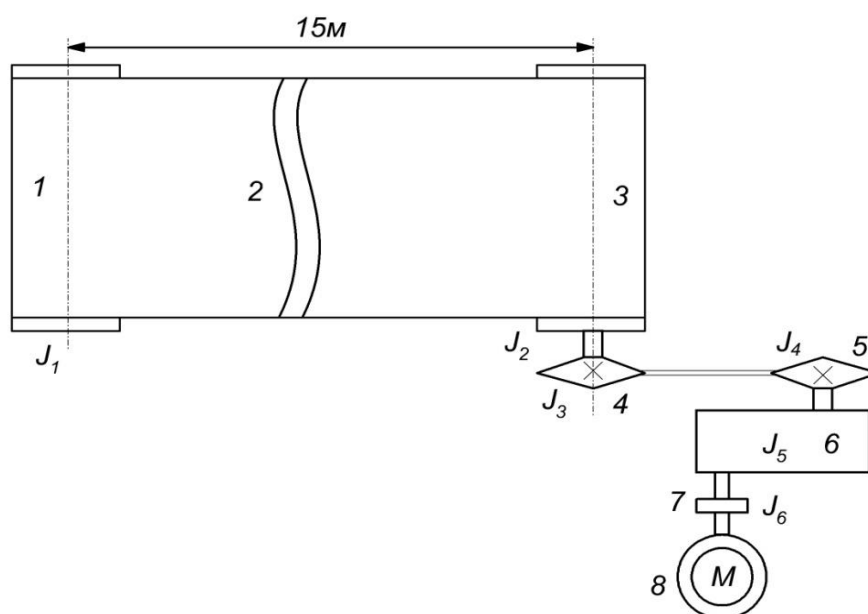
Кінематична схема приводу сітчастого поду (1- натяжний барабан; 2 – сітчастий под; 3 – приводний барабан; 4,5 – ланцюгова передача; 6 – редуктор циліндричний; 7 – напівмуфта сполучна; 8 – електродвигун).
